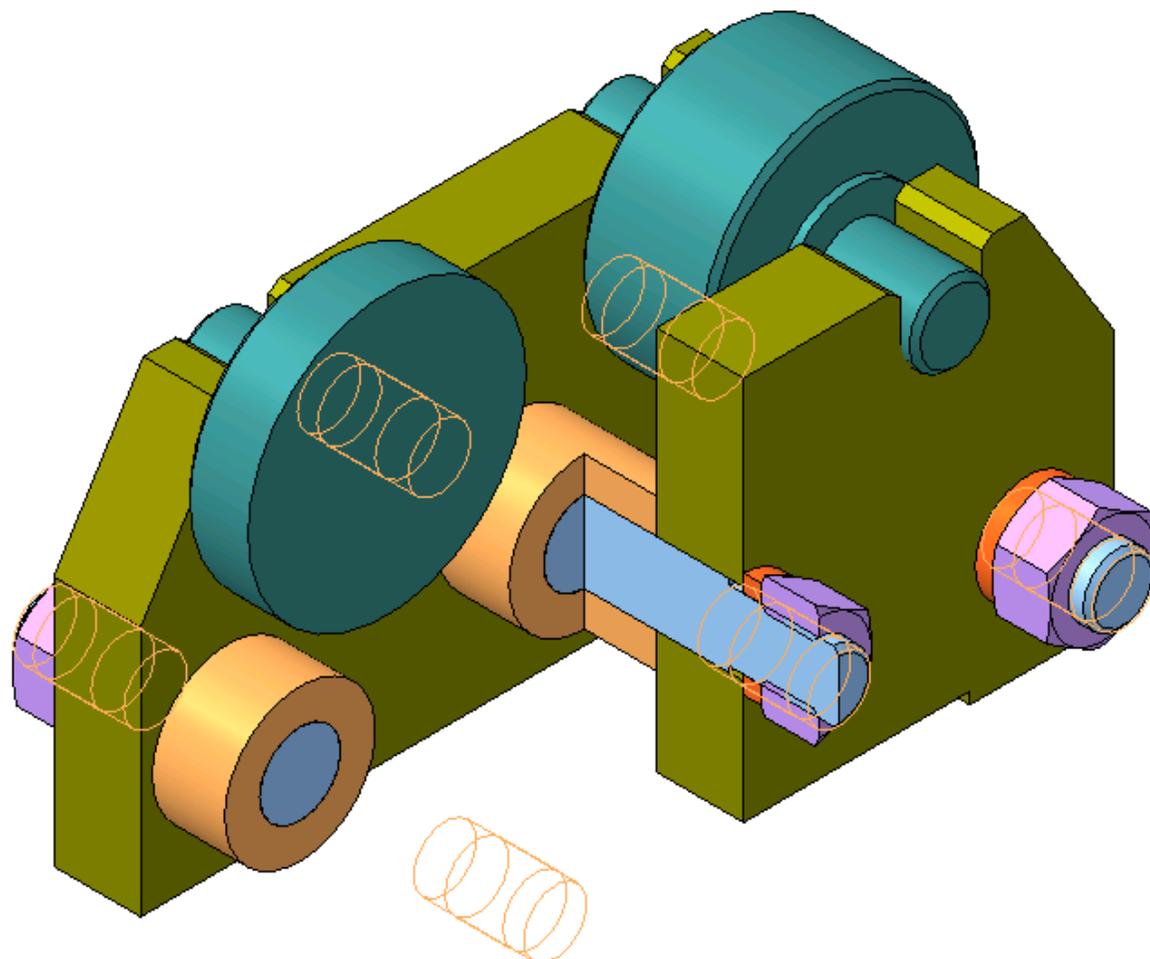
3D-модель сборки изделия «Опора роликовая» (варианты 13, 33)
